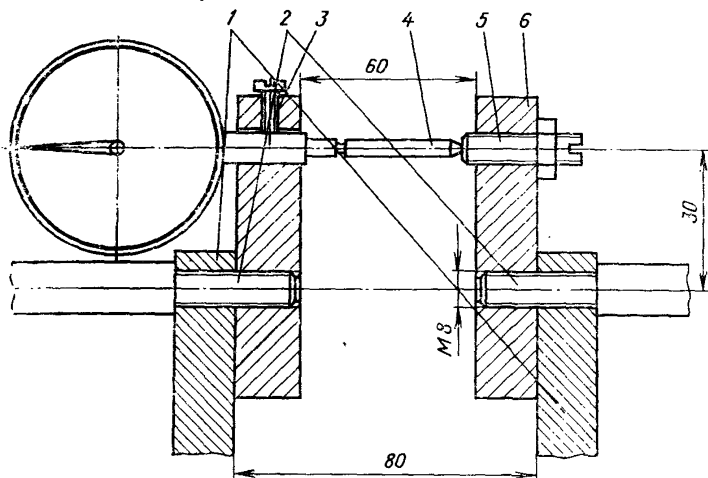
Приспособление для установки микатора в тензомере: 1, 2 — щеки и шпильки тензомера; 3 — стопорный винт для установки индикатора; 4 — удлинительная проставка; 5 — регулировочный винт с кернением; 6 — пластина для установки индикатора
